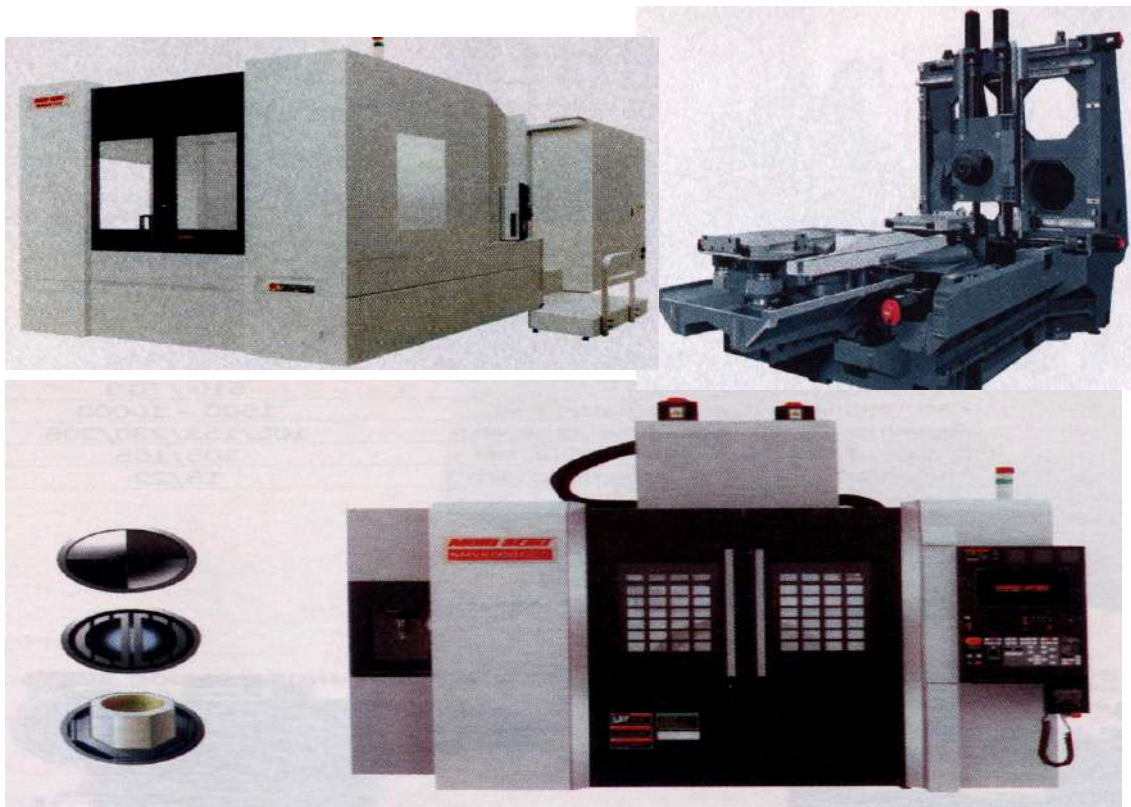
Фрезерні вертикальні верстати серії *RL
